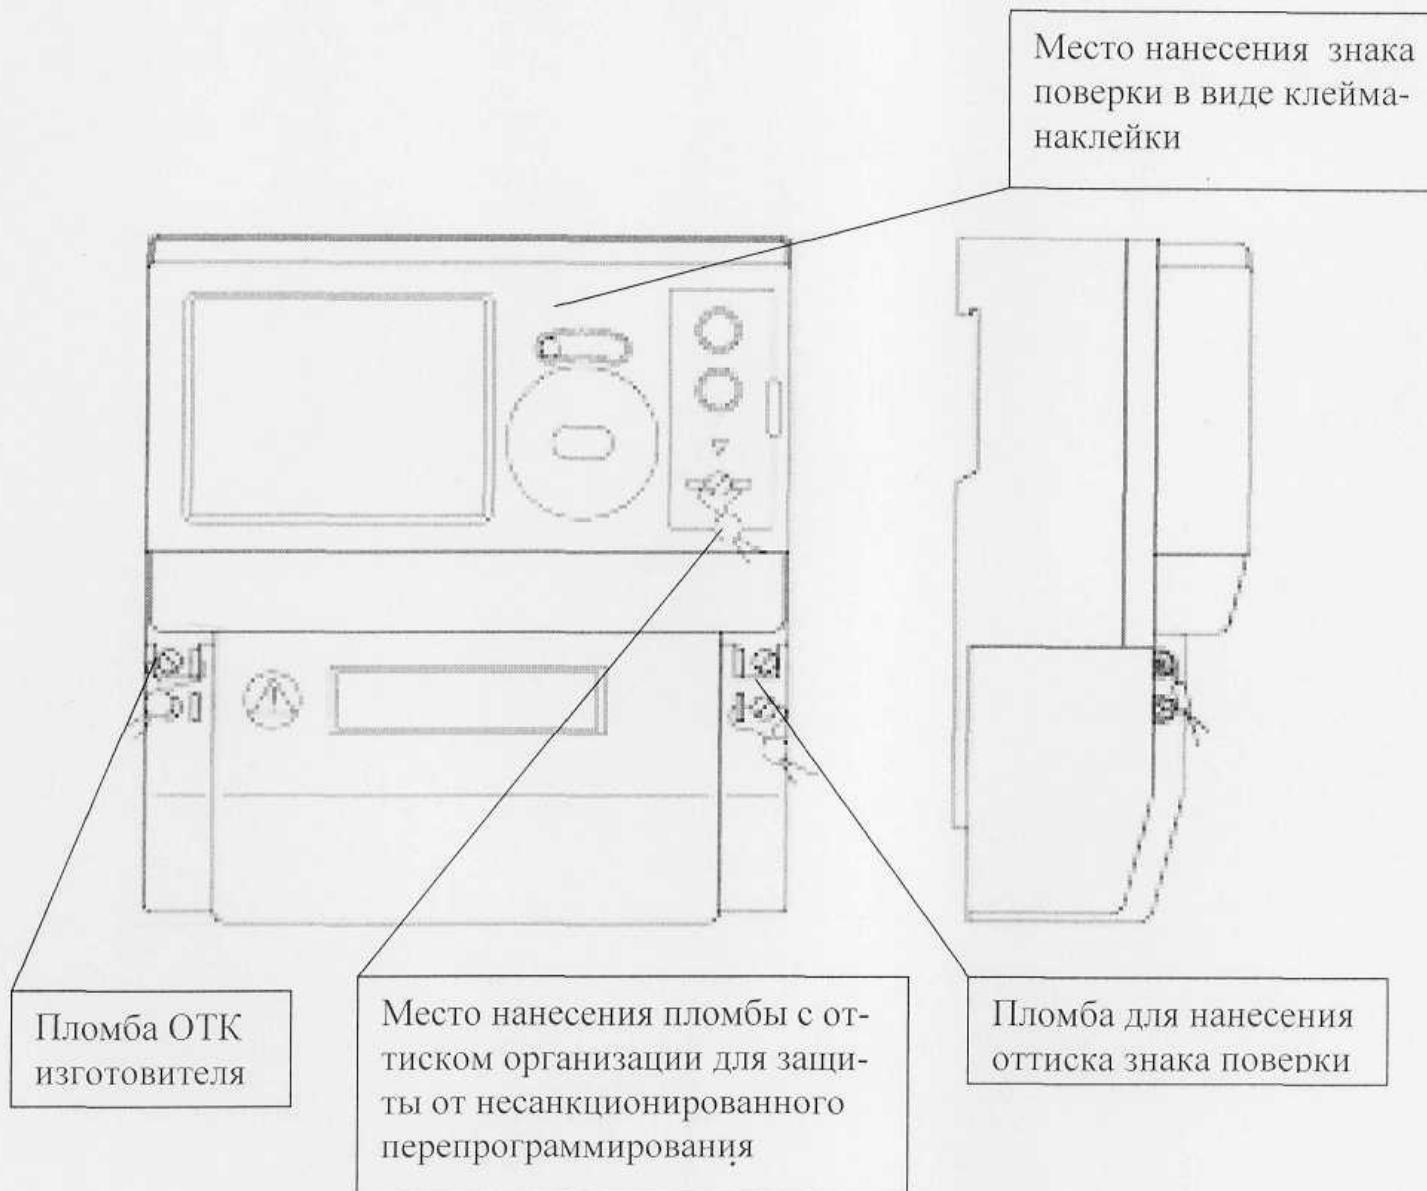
Корпус счетчиков СЕ301ВҮ SX XXX XXXXX
